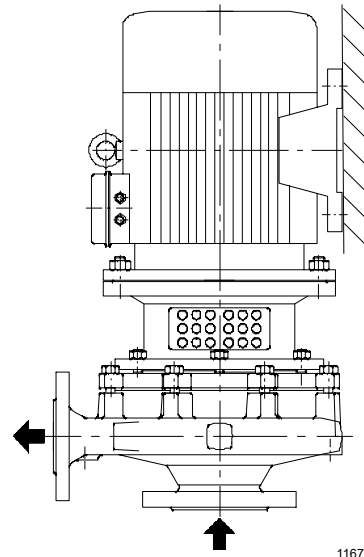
Motorfuß Befestigung seitlich, Motorgröße
